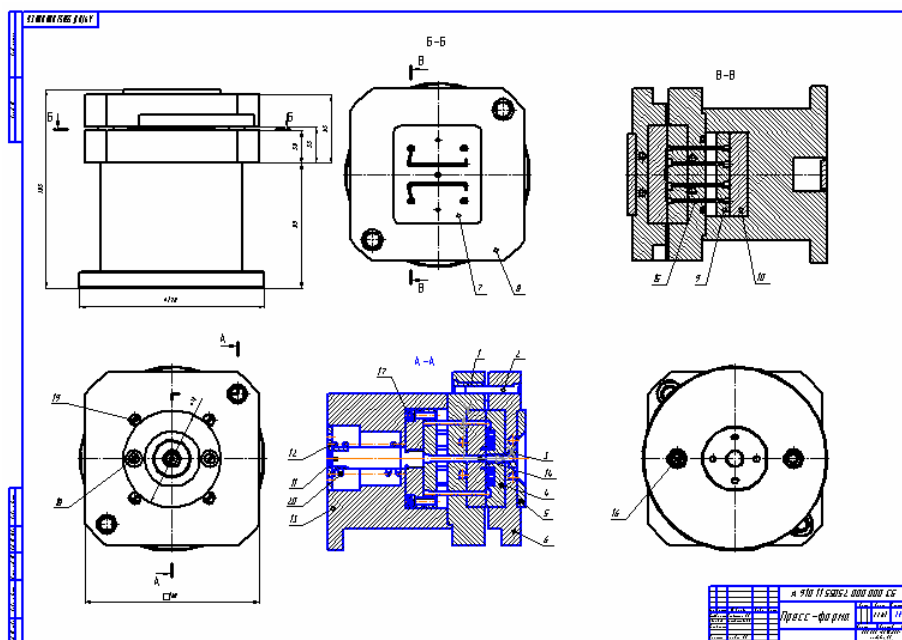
Чертеж пресс-формы в сборке, сгенерированный по 3D-модели
